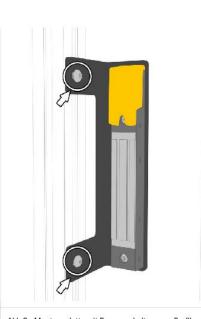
Montageplatte mit Prozesszuhaltung am Profil anbringen und und Schrauben M8 x 12 mm Torx festziehen.
